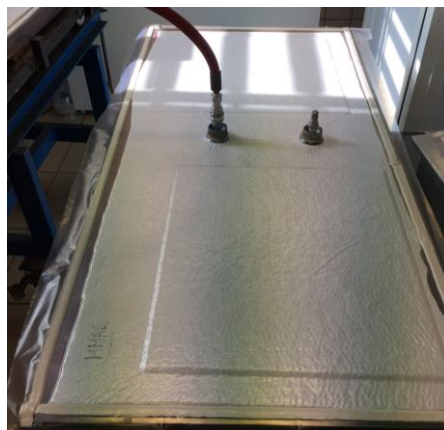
Apilado del laminado rígido del panel de tejido.
